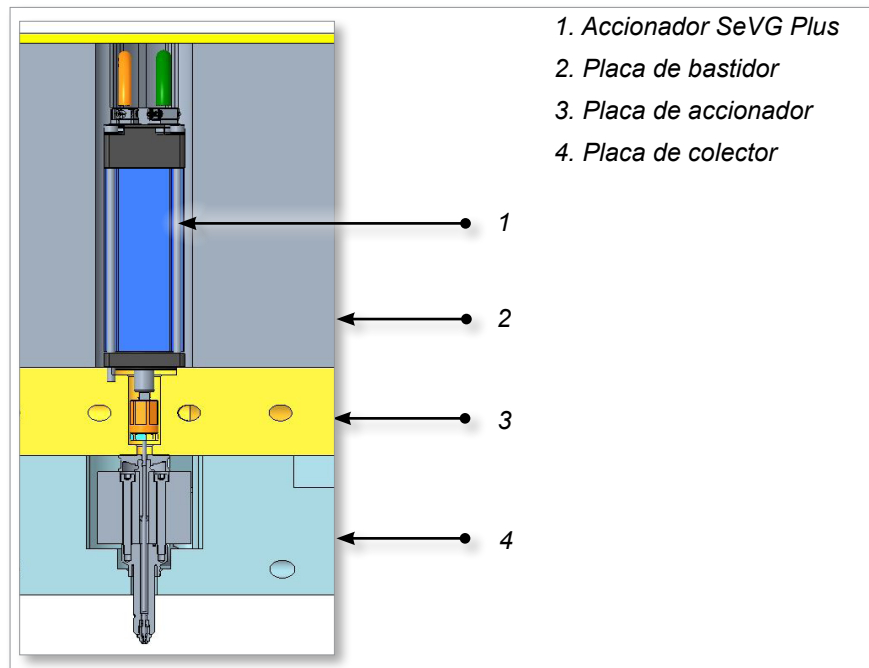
Accionador SE20-15 en un sistema de canal de colada caliente
